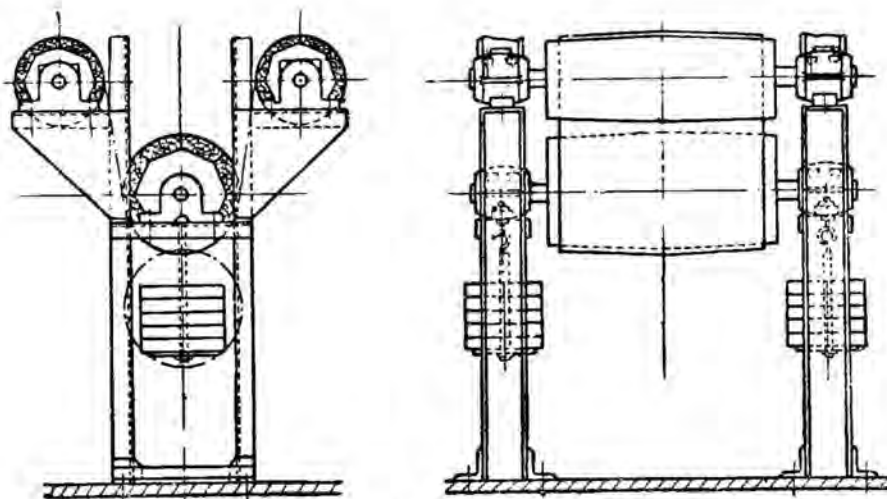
Вертикальное грузовое натяжное приспособление Горзавтреста.
